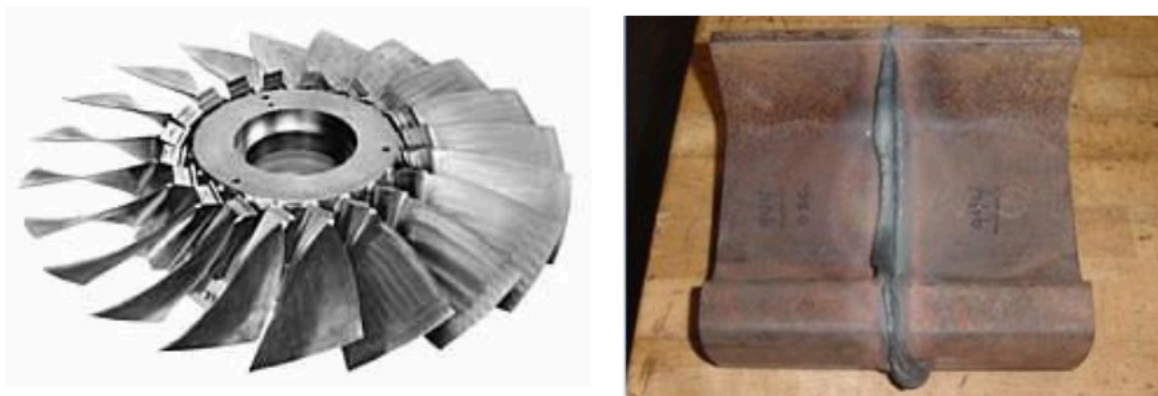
Blisk (izq.) y vía férrea (der.) soldados mediante LFW. [31]
